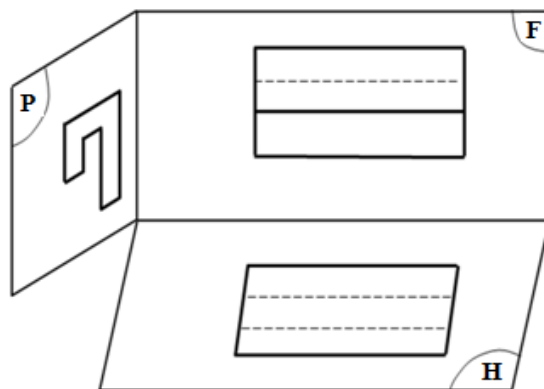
Projections orthogonales dans trois plans perpendiculaires entre eux
